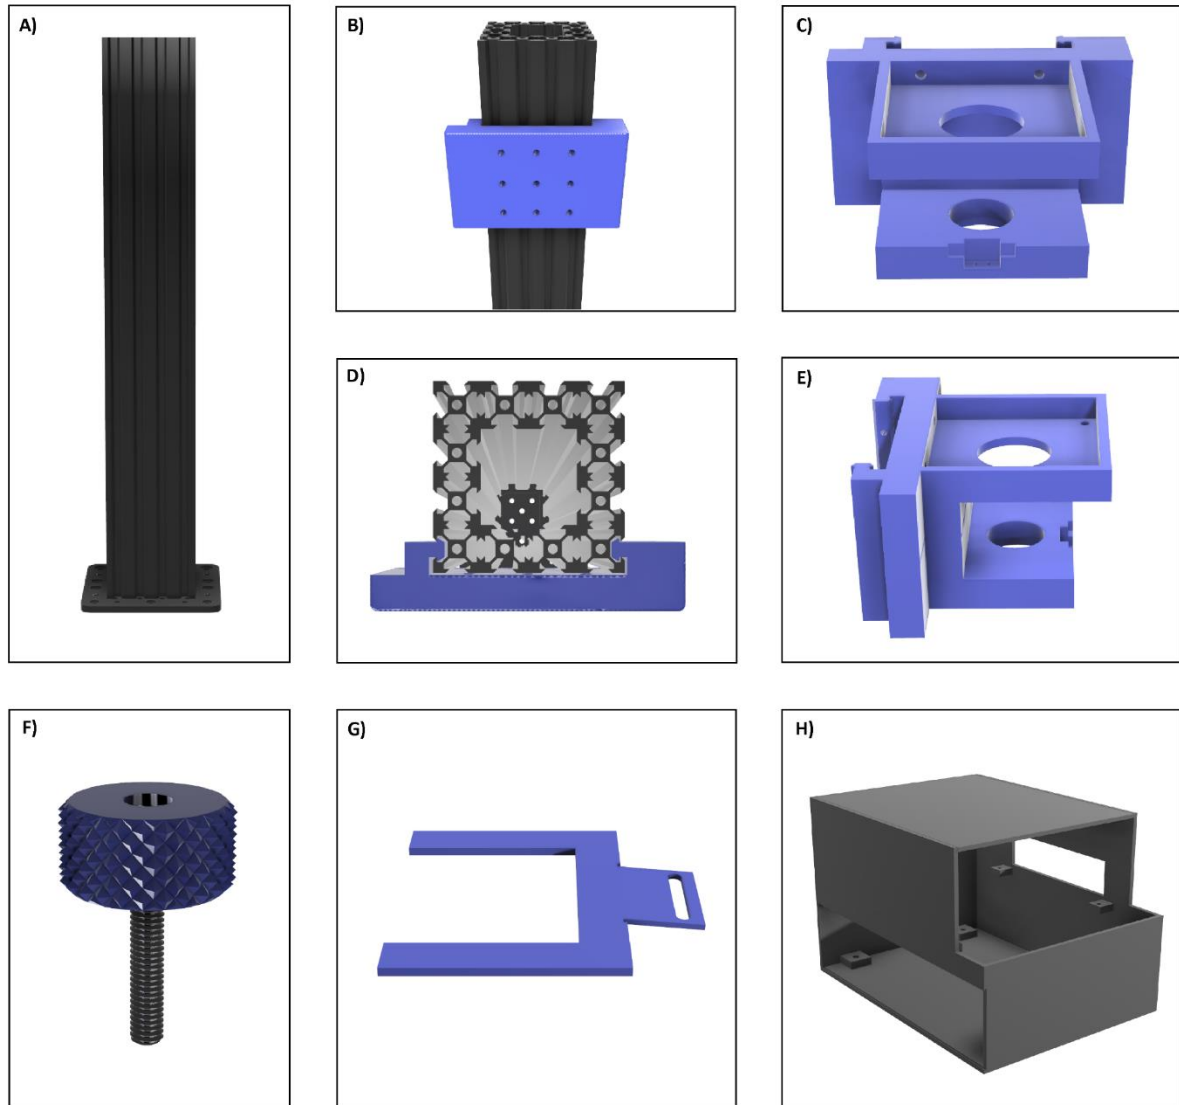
Diseño de piezas tridimensionales en Fusion 360. A) Diseño de la torre guía, que fue generado únicamente para mejorar la precisión de las otras piezas. B) Diseño plataforma de montaje ubicada sobre la torre guía. C) Diseño plataforma de montaje especial para alojar el actuador lineal y la muestra. D) Vista superior de la torre y plataforma de montaje, permite visualizar los carriles (V-Slots) involucrados en el desplazamiento a lo largo de la torre guía. E) Vista lateral de la plataforma de montaje especial para el actuador lineal. F) Diseño de la perilla, que permite fijar las monturas en la torre guía. G) Diseño porta-muestras, que irá anclado al micro ajustador horizontal. H) Diseño de la carcasa para el circuito del actuador lineal y para su fuente de poder. Los diseños de cada pieza han sido incluidos en formato digital en anexos.
